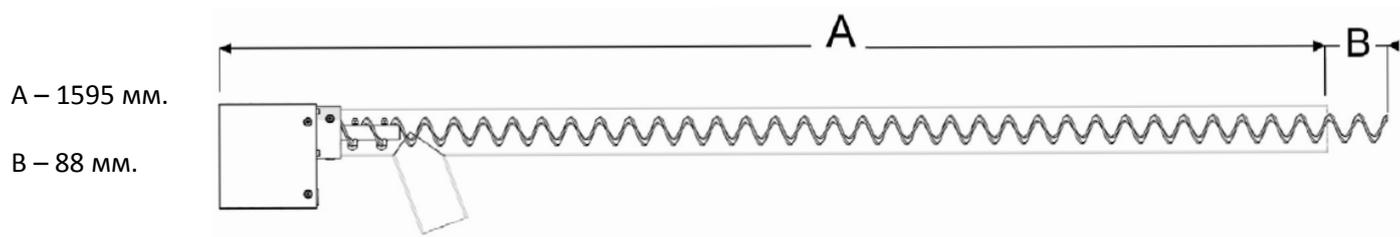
Схема размеров питателя (устройства подачи топлива)
